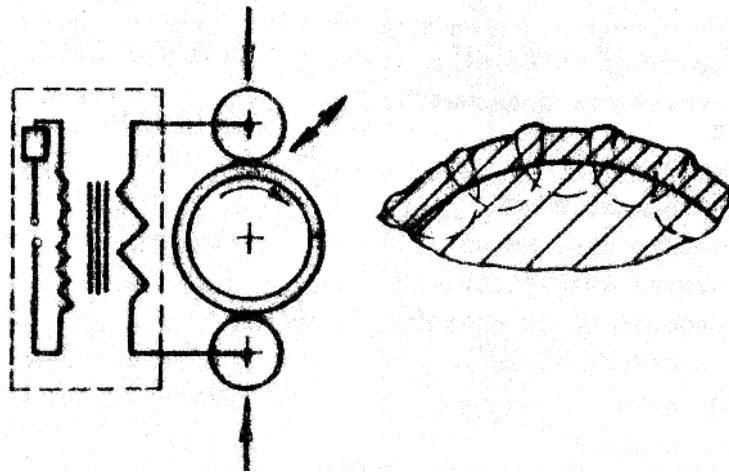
Схема наварювання стрічки на деталь типу “вал” і перекриття імпульсів при наварюванні
